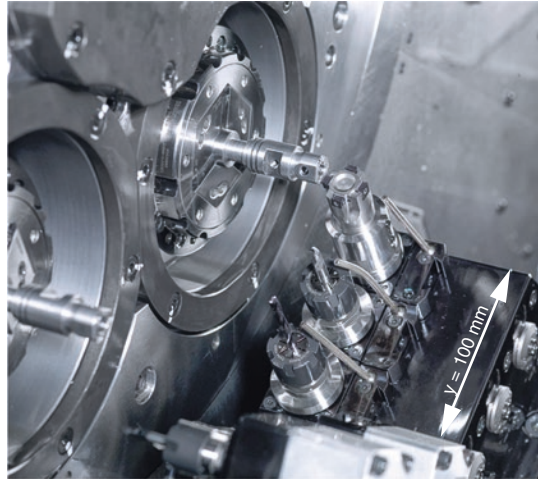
Bearbeitungseinheit mit y-Achse und drei Werkzeugen, hier alle angetrieben [Dmgm17]
